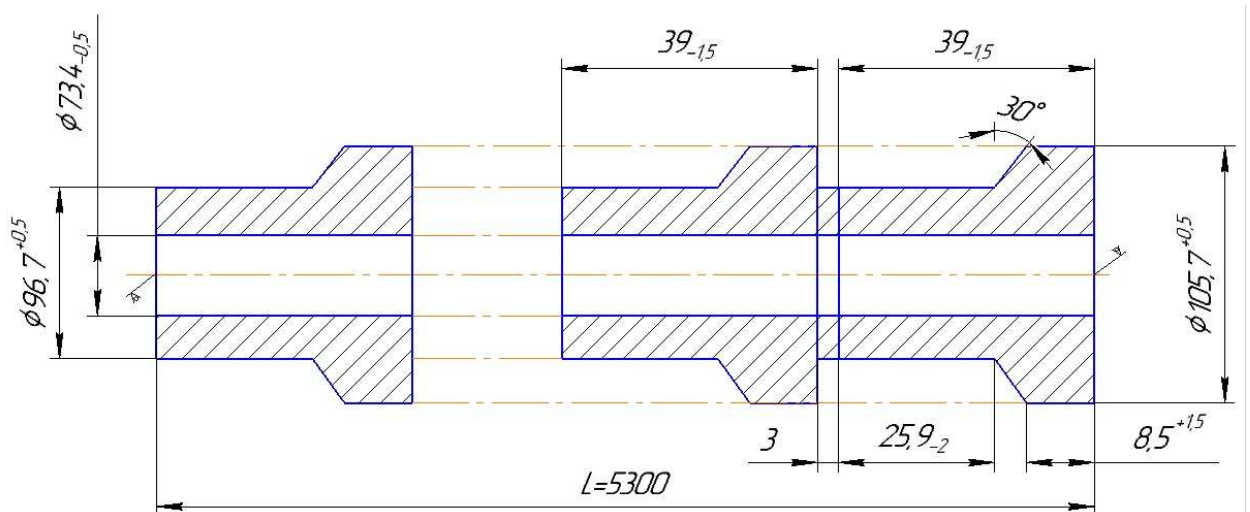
Операционный эскиз длинномерной трубной заготовки (ДТЗ) с РПП и припусками под механическую обработку ВК: $L = 5300$ – длина трубной заготовки; $\varnothing 105,76$ – диаметр наружной поверхности РПП; $\varnothing 97,6+0,5$ – диаметр наружной дорожки; $\varnothing 73,4$
